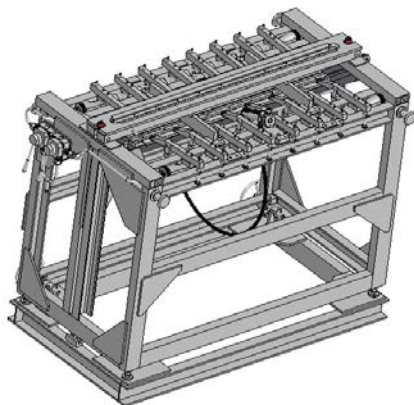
Приспособление для сварки продольных швов
